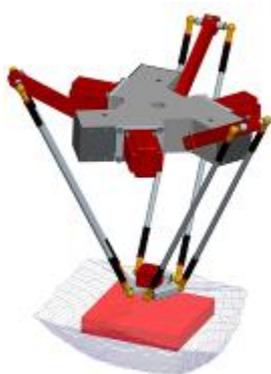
ДЕЛЬТА-механизм с поворачивающимися шарнирами
